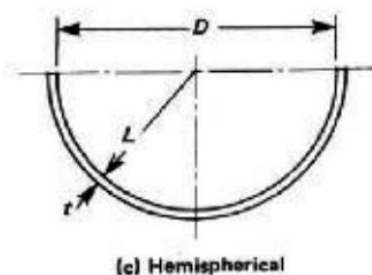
Dimensiones de un cabezal hemisférico. Fuente:(15)
